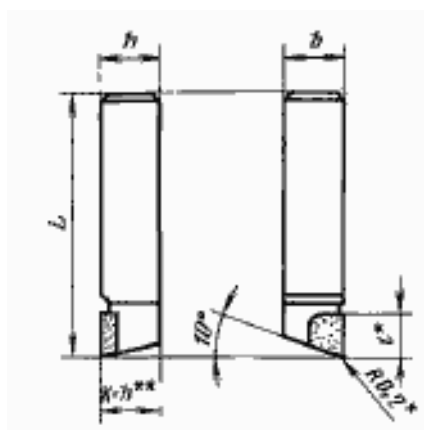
Резец расточной державочный с напаянными пластинами из твердого сплава ГОСТ 9795-84
